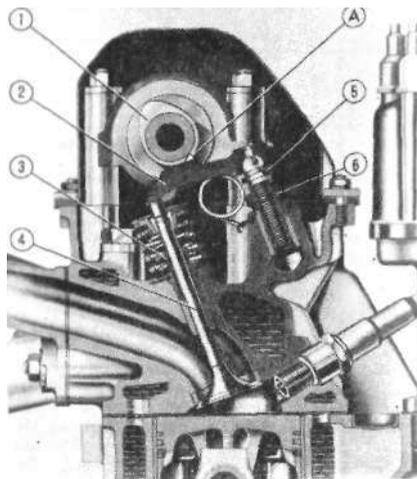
Механизм газораспределения: А — зазор между рычагом и кулачком; 1 — кулачок распределительного вала; 2 — рычаг привода клапана; 3 — маслоотражательный колпачок клапана; 4 — клапан; 5 — регулировочный болт рычага; 6 — контргайка регулировочного болта
